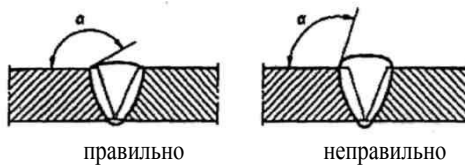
28. Неправильный профиль сварного шва
